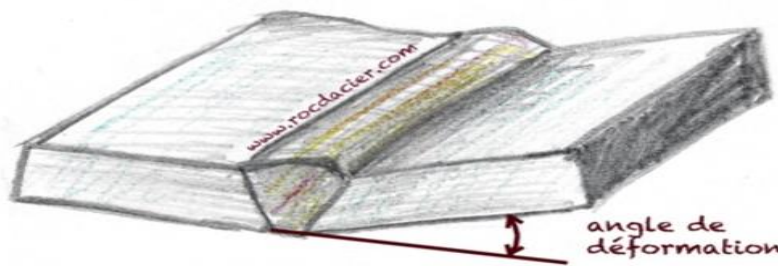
angulaires dans un joint soudé (Réf.[R28])
